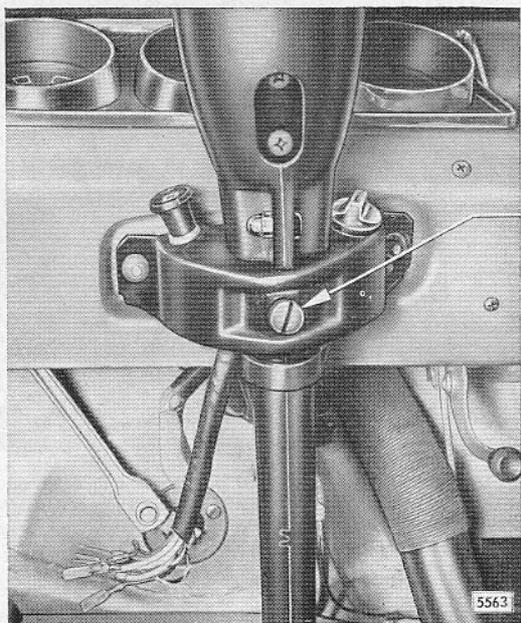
Anschlagsschraube für Lenkspindel im Lenkstützrohrhalter
